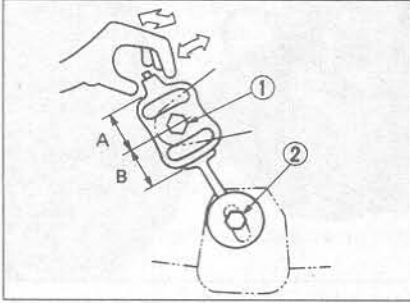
Регулировка переднего буферного стержня двигатель/трансмиссия (Глава 10)
